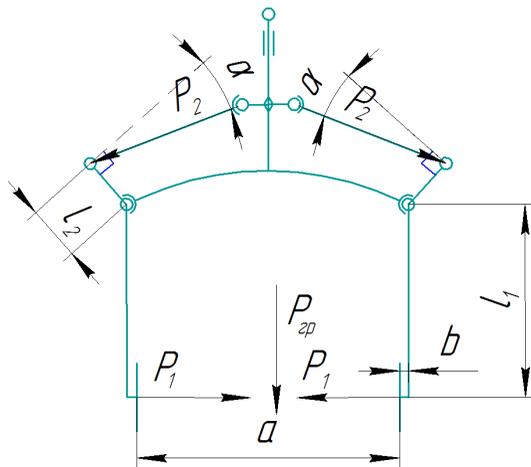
Расчетная схема универсального грузозахватного устройства
